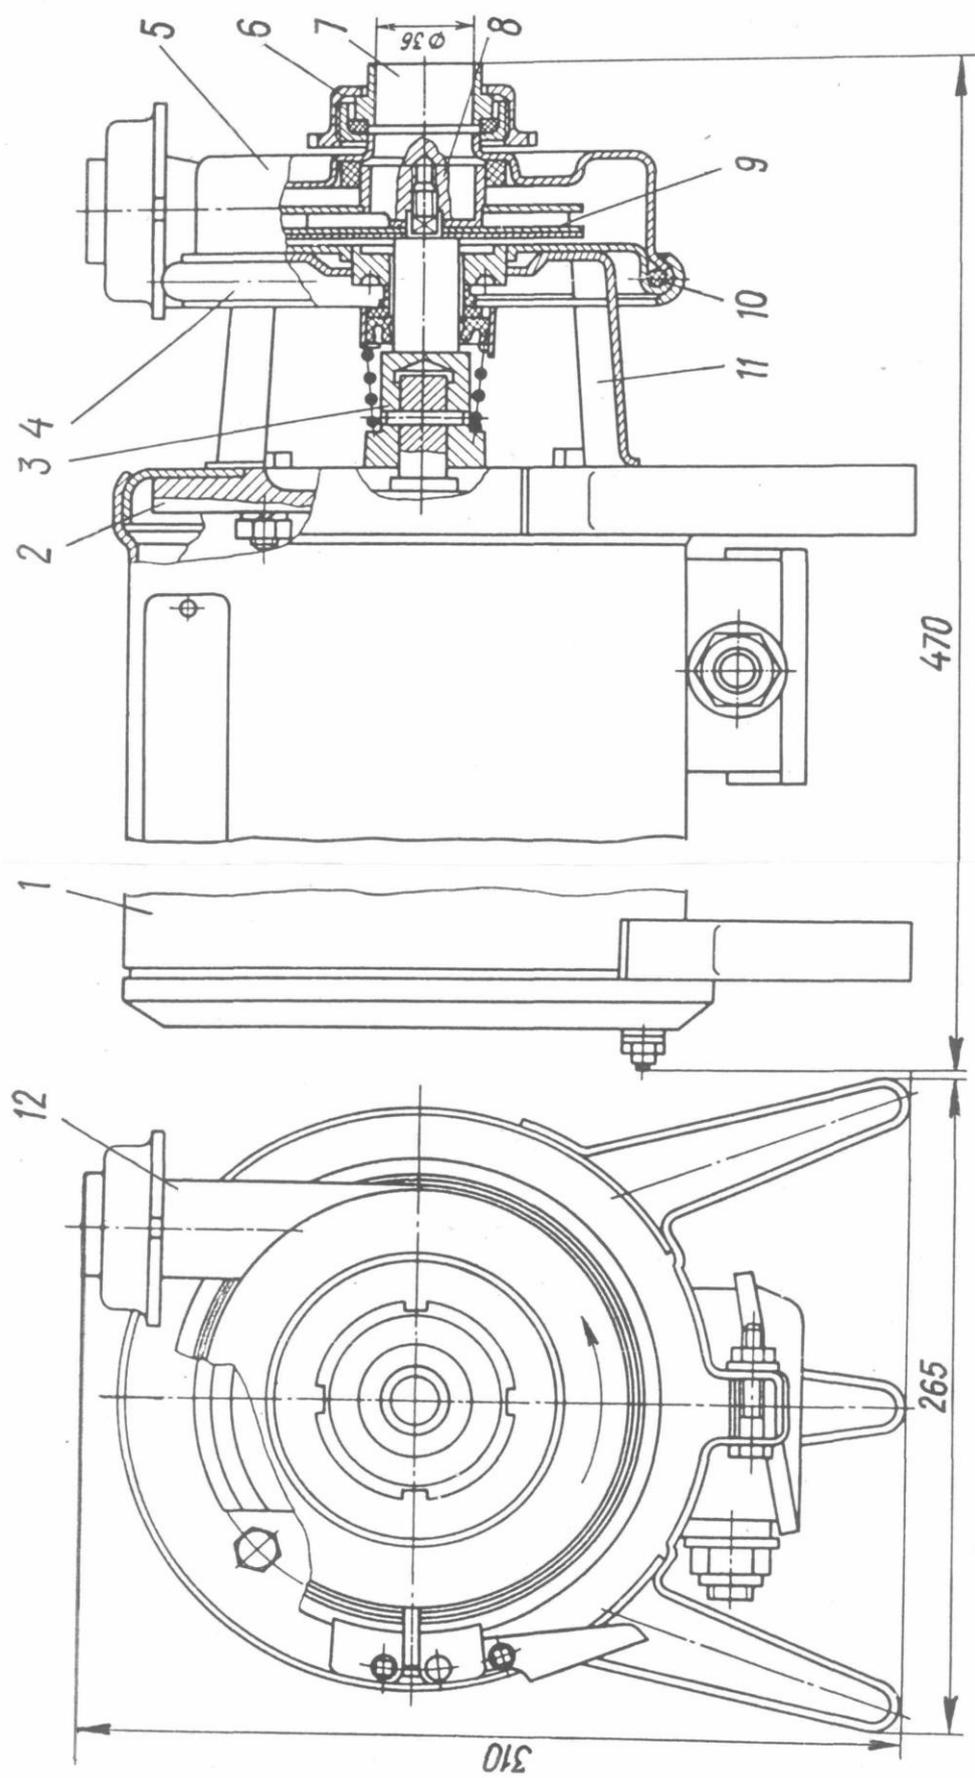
Конструкция электронасоса центробежного типа 36-1Ц2, 8-20 марки Г2-ОПБ: 1 – кожух; 2 – электродвигатель; 3 – наконечник; 4 – зажимное кольцо; 5 – корпус; 6 – накидная гайка; 7 – штуцер; 8 – гайка; 9 – рабочее колесо; 10 – уплотнительное кольцо; 11 – кронштейн; 12 – штуцер
